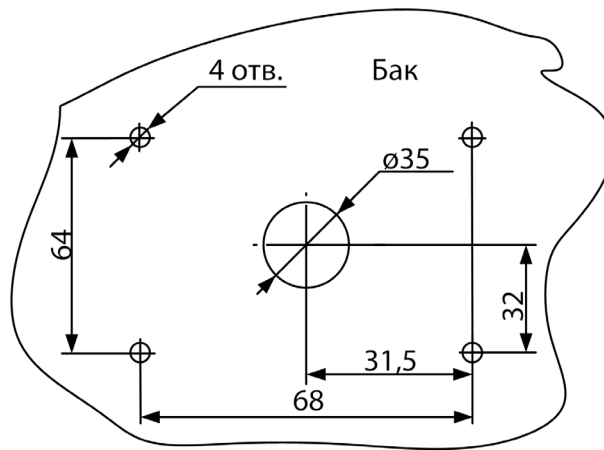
Подготовка места установки датчика Omnicomm LLS
